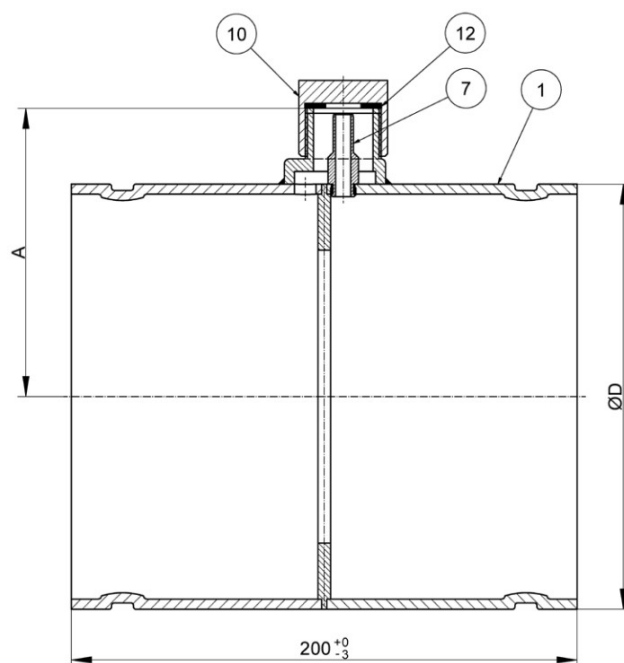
Placa de orifício GT-FluxFP, Desenho e dimensões 6"/DN 150 - 12"/DN 300
